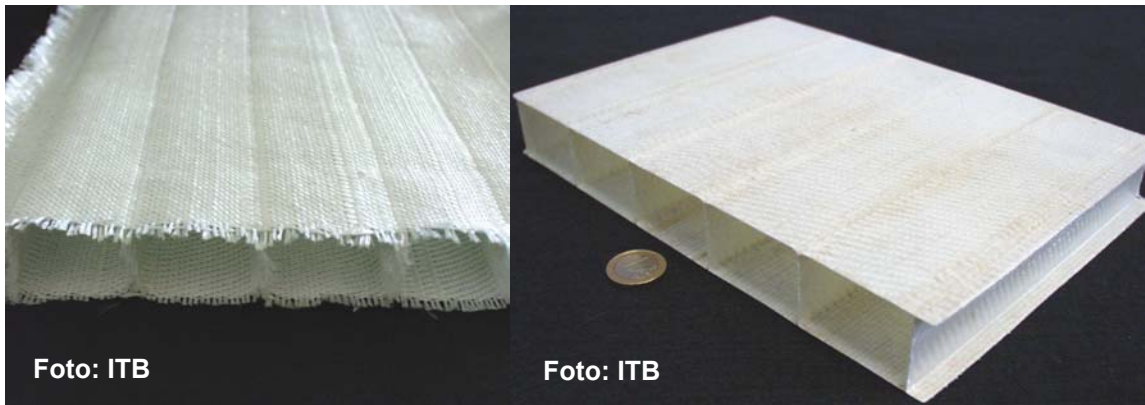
ITB: Gewebtes spacer fabric mit gewebten Stegen (links) und thermo-gepresstes Bauteil (rechts)
